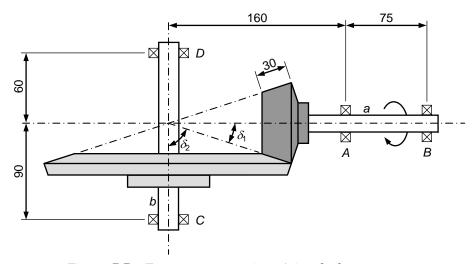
Engrenagem exterior cónica de dentes retos.
